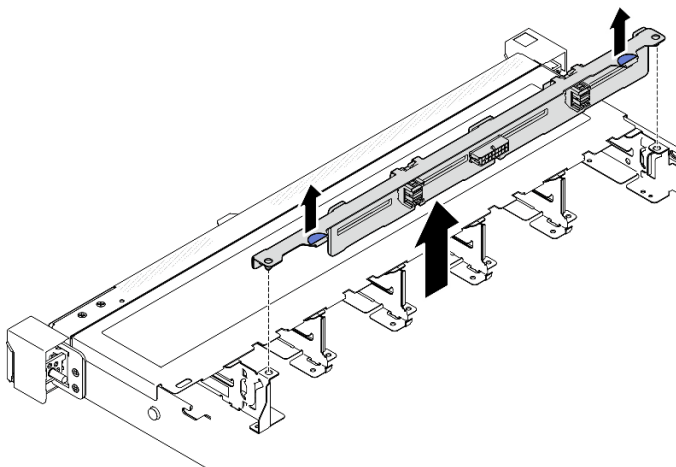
Remoção do backplane com oito unidades hot-swap de 2,5"
